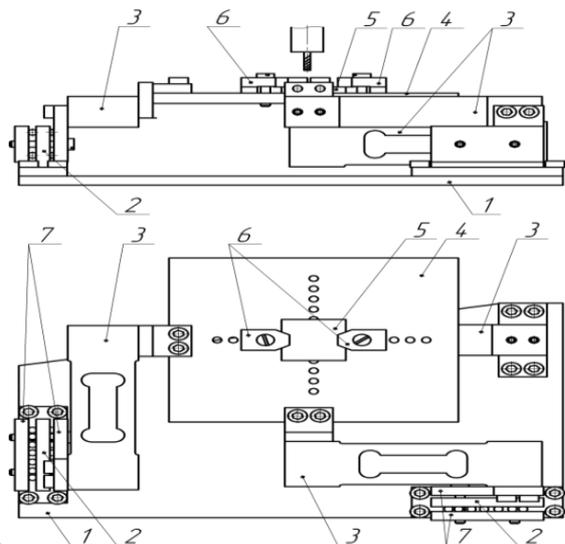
Компонновка устройства для измерения сил резания при обработке мелкогабаритным инструментом: 1 – основание, 2 – неподвижные стойки, 3 – датчики, 4 – пластина, 5 – заготовка, 6 – прихват, 7 – направляющие
